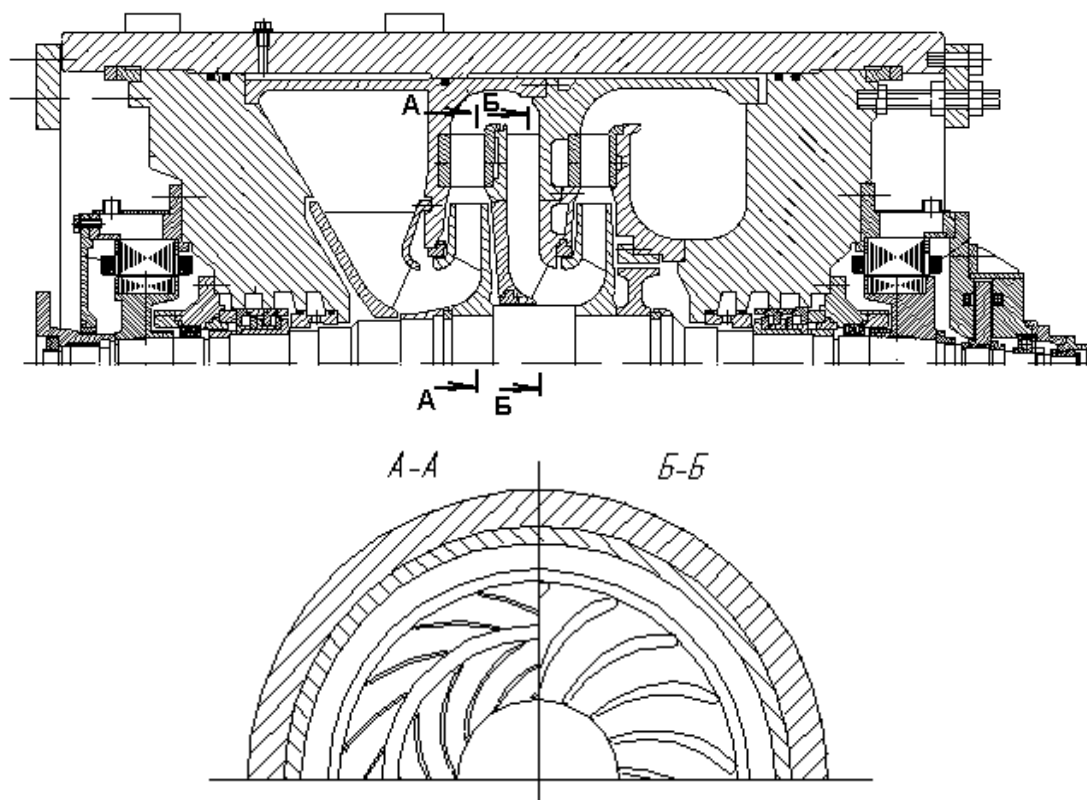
Двухступенчатый центробежный компрессор высокого давления.
